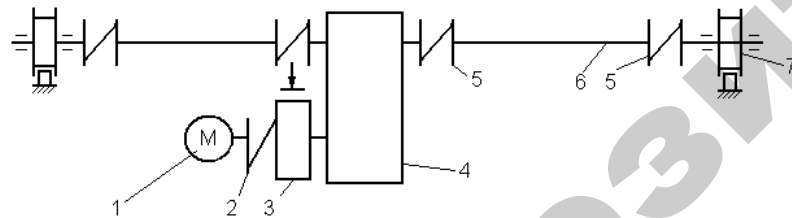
Кинематическая схема привода механизма передвижения мостового крана: 1 – электродвигатель 4АС71А693; 2 – муфта МУВП; 3 – тормоз ТКТ-100; 4 – редуктор Ц2У-100; 5 – муфты соединительные типа МЗ; 6 – вал торсионный; 7 – колесо ходовое
